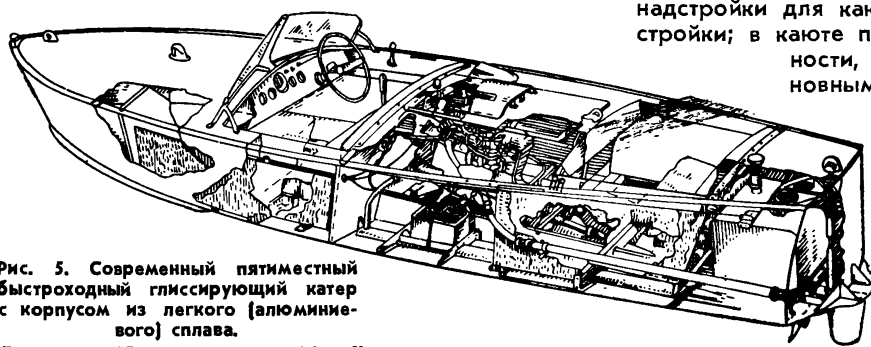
Современный пятиместный быстроходный глиссирующий катер с корпусом из легкого (алюминиевого) сплава.
